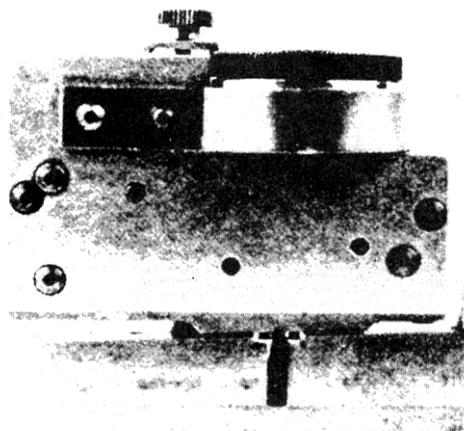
Типичный индикаторный прибор для контроля упорной резьбы
